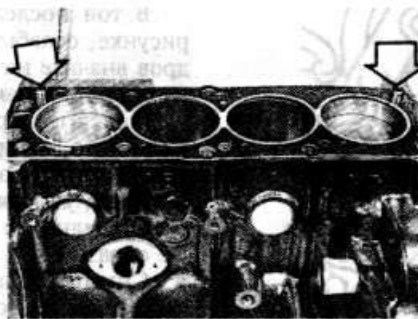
Прокладка головки блока цилиндров установлена правильно на штифтах (показаны стрелками) на блоке цилиндров — двигатель 1,6 л (двигатель снят с автомобиля)
